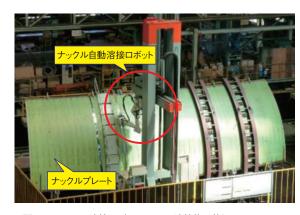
ナックル溶接ロボットによる溶接施工状況 Fig. 5 Welding with automated knuckle plate welding robot
